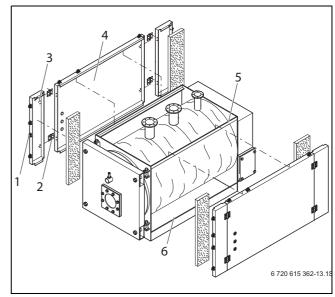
Монтаж боковых стенок в котлах 120 кВт - 420 кВт
